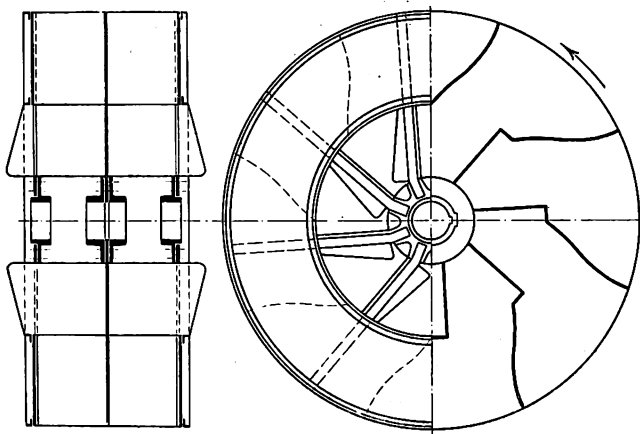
bis 29. Ventilator der Zeche Dorstfeld für 8328 cbm/min.
